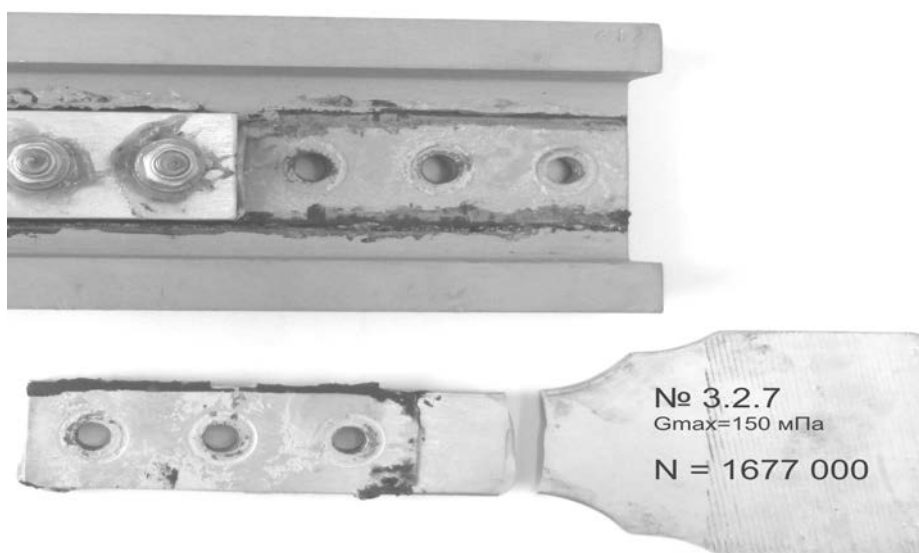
Вид на поверхности контакта полосы и профиля односрезного образца, обработанных круговым барьерным обжатием и покрытых полимерным наполнителем ВЗ-27м после усталостного разрушения
